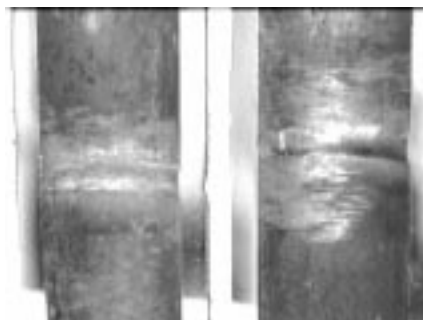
Macrografía interior de la Soldadura Orbital
